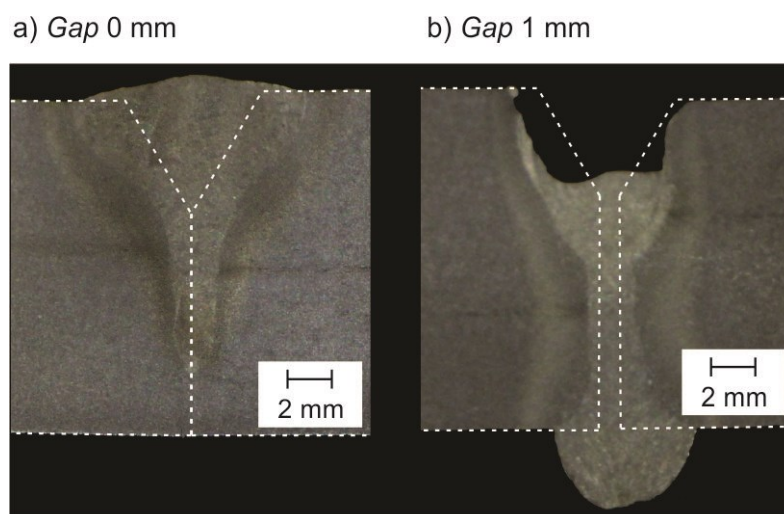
Macrografia de solda realizada pelo processo HLAW aplicado em junta com utilização de *backing* com abertura de junta de a) 0mm e b) 1mm. (Fonte: Autor)
